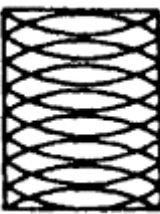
Общий вид образцов шероховатости,поставляемых отдельными образцами
